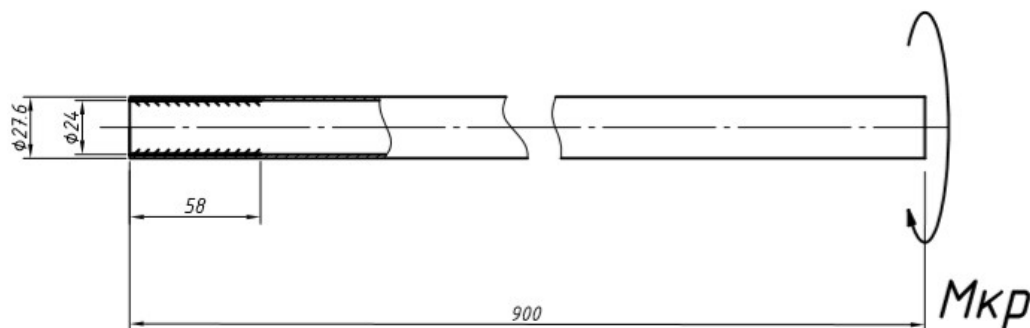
Розрахункова схема карданного валу нової конструкції другого типорозміру
